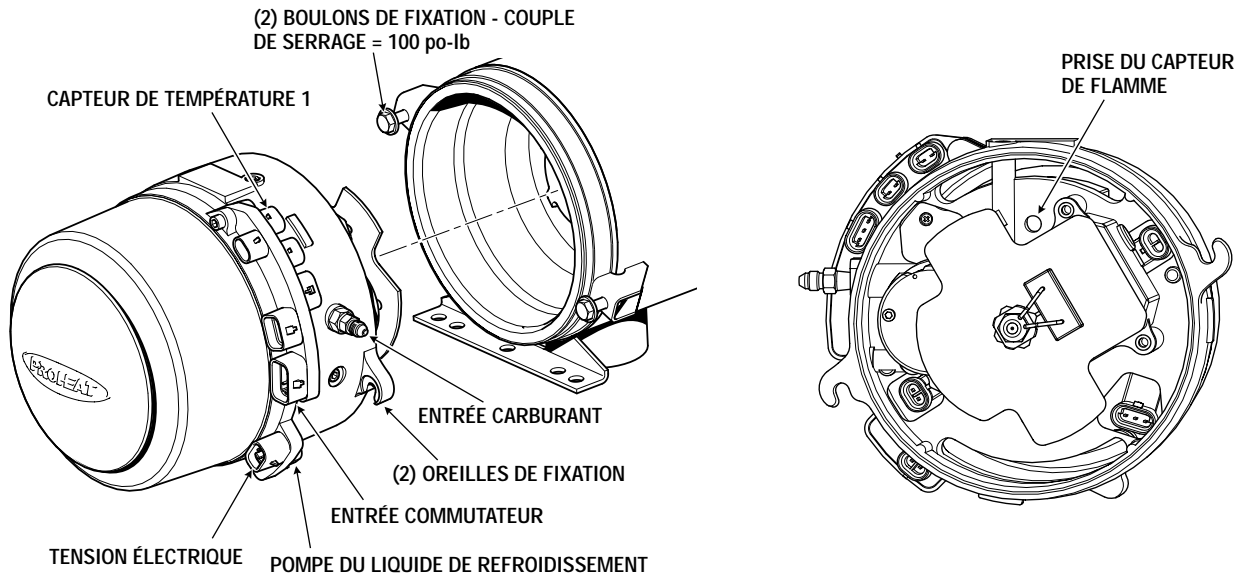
Démontage de la tête de combustion et emplacement du capteur de flamme
